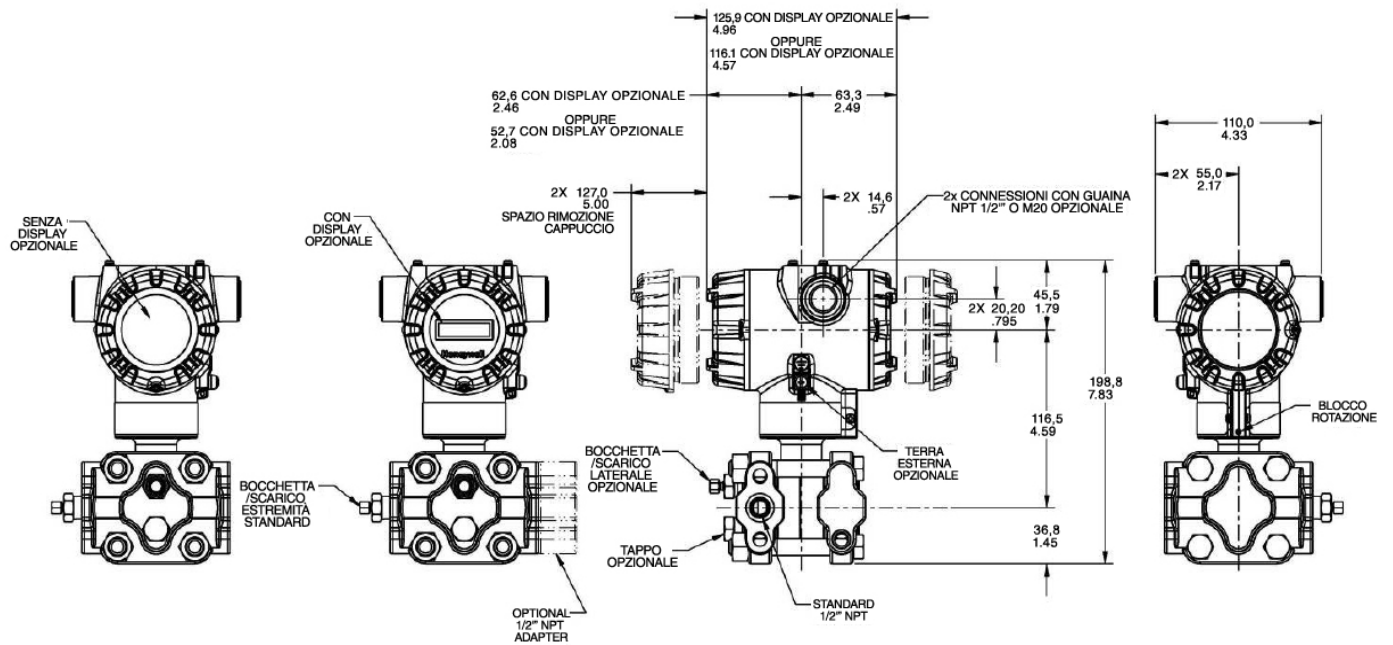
Dimensioni di montaggio tipiche di STG740 e STG770 solo per riferimento
